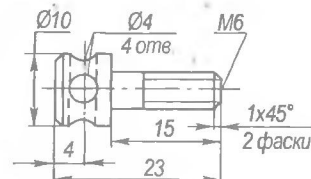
Специальный болт для крепления клапана к цилиндру двигателя Д-8
